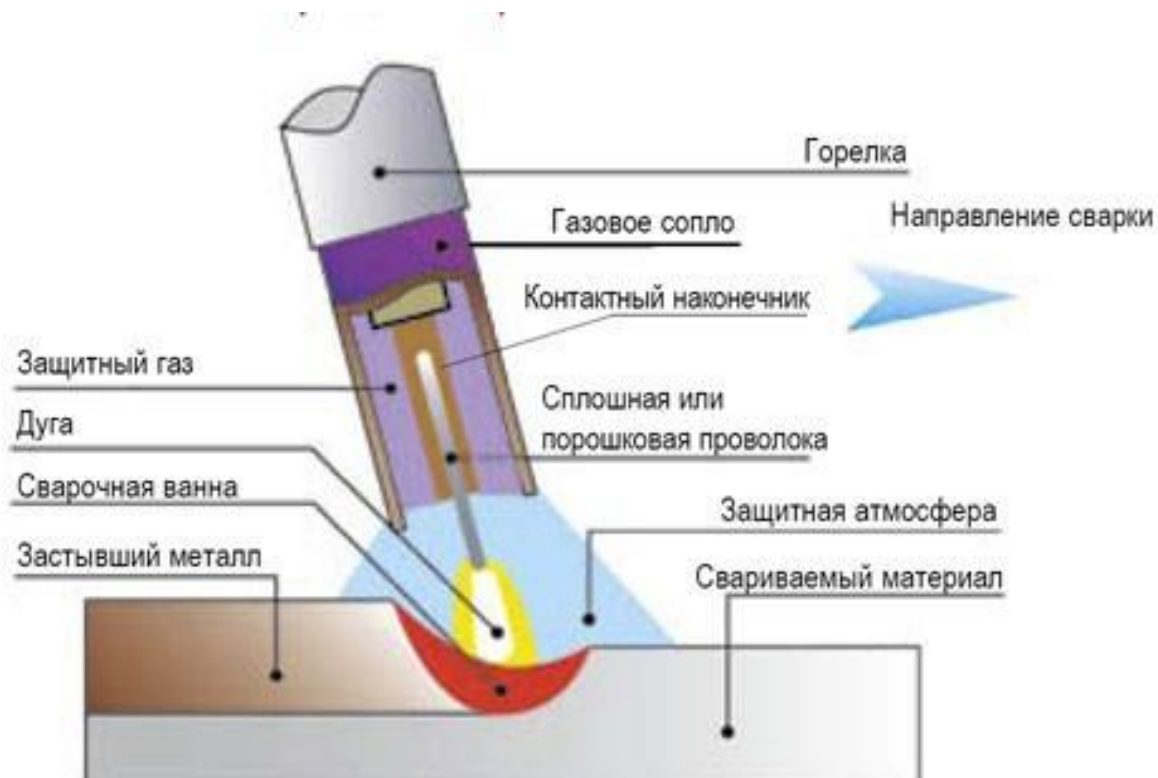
Схема механизированной сварки в защитных газах
